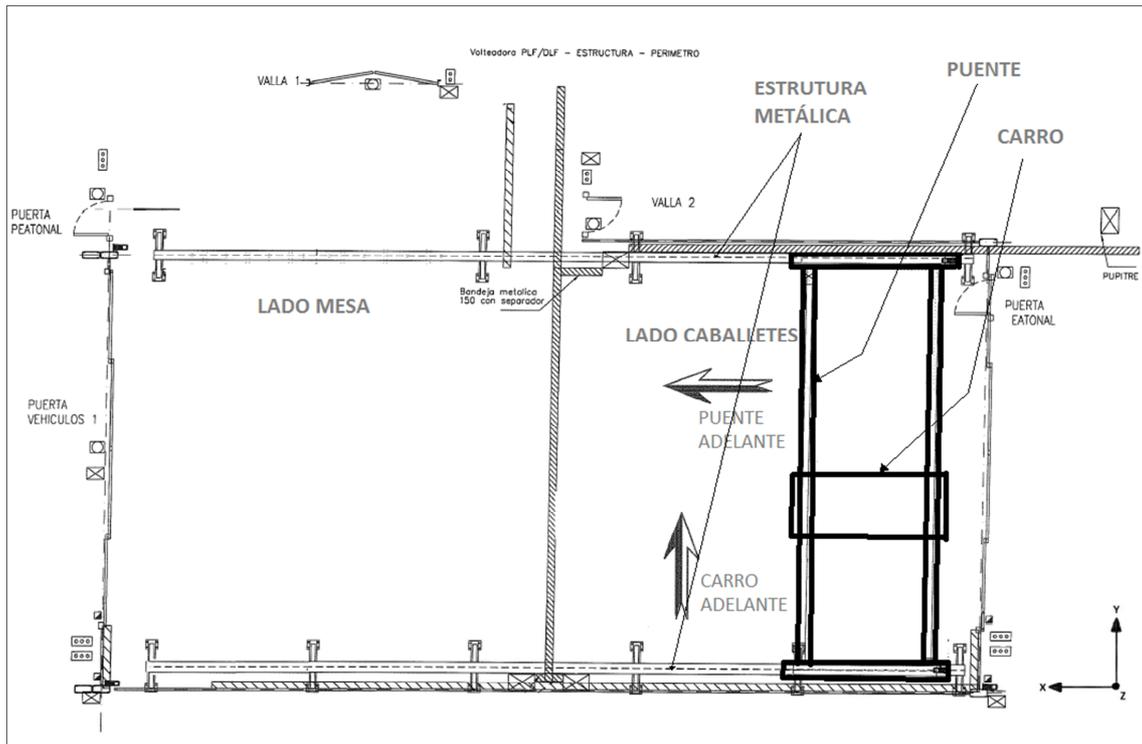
Esquema en planta de la volteadora de entrada. Situación y movimiento del puente y el carro.
